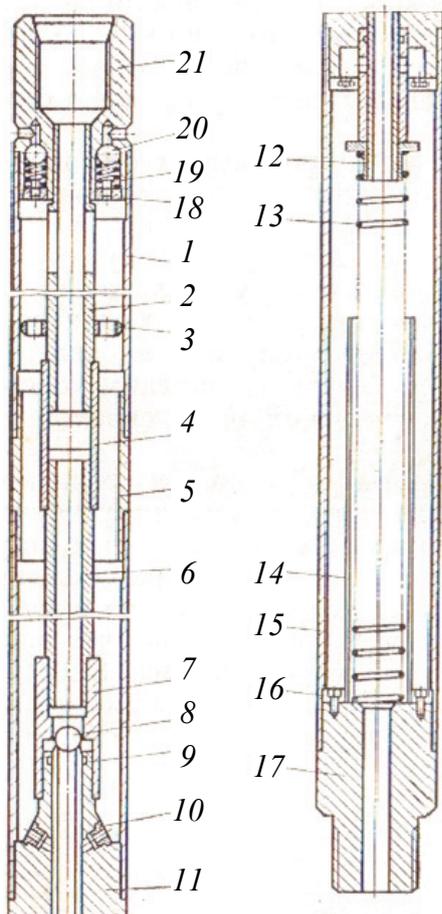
Скважинный смеситель типа СС-89: 1, 2, 6, 15 – труба; 3 – центратор; 4, 5 – nipple; 7 – муфта; 8, 20 – шарик; 9 – уплотнительное кольцо; 10 – штуцер; 11, 17, 21 – переходник; 12 – шток; 13, 19 – пружина; 14 – гильза; 16 – винт; 18 – заглушка
